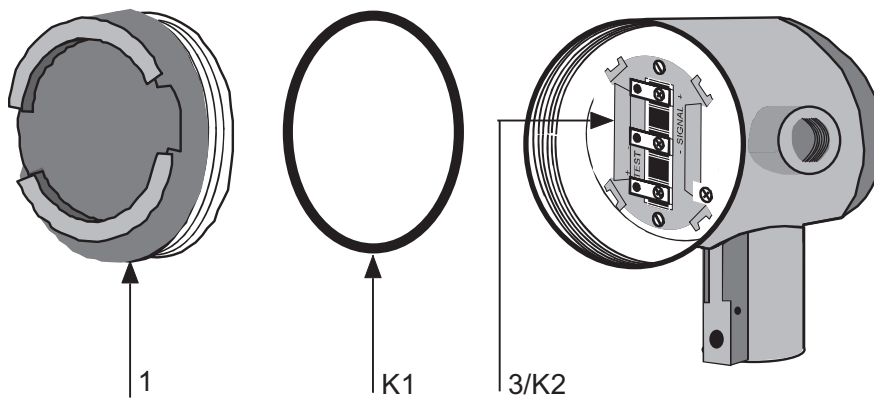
Корпус электроники преобразователя серии 100/900 со стороны клеммного блока
